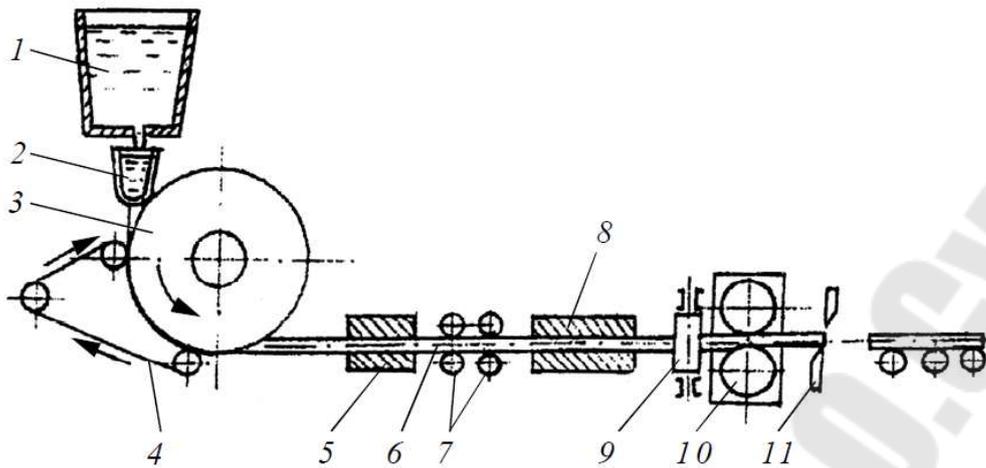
Схема литейно-прокатного агрегата для получения сортового проката:
